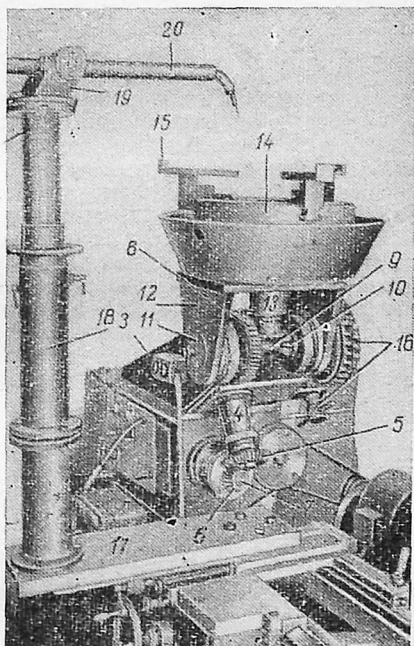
Передняя бабка и рабочая штанга на подъемной колонке универсального сварочного станка.
